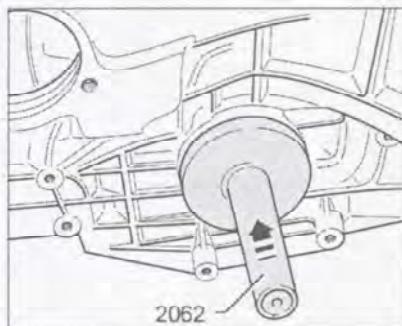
С помощью специального инструмента запрессуйте новый сальник приводного вала.
